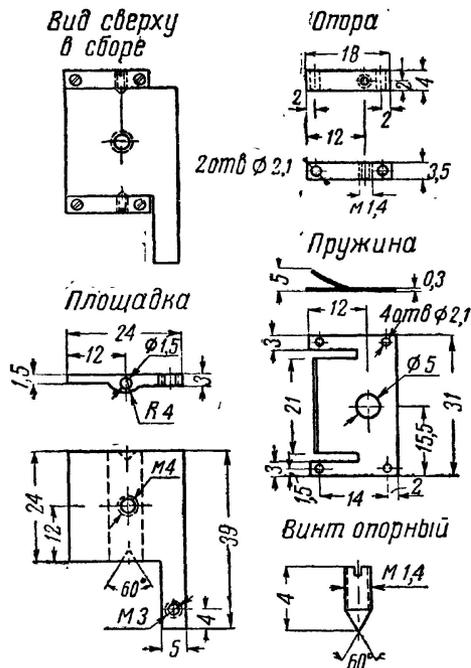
Детали для регулировки положения головки: площадка (дюраль Д16Т) — 1 шт.; опора (дюраль Д16Т) — 2 шт.; пружина (пружинная сталь 65Г) — 1 шт.; винт опорный (сталь Ст-45) — 2 шт.; винт крепления М2×9 (сталь 3) — 4 шт.; винт регулировки М3×8 (сталь 3) — 1 шт. Для каждой головки необходимо изготовить по одному комплекту таких деталей
